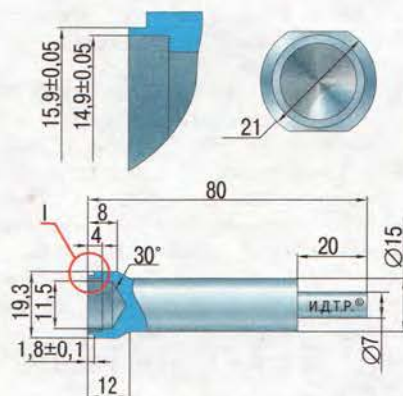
Оправка для сборки гидронатяжителя цепи
